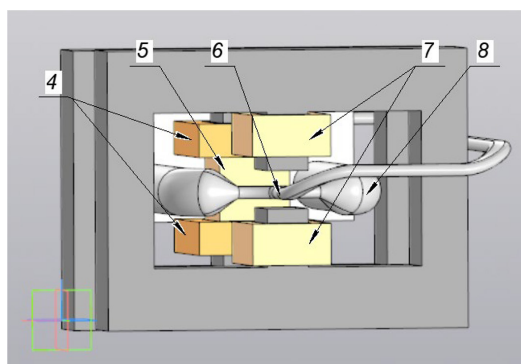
Конструкция электромагнитного насоса, вид спереди (футеровка скрыта), где: 4 – дополнительные катушки основного индуктора; 5 – основной индуктор; 6 – тройниковая рабочая зона; 7 – катушки электромагнита; 8 – жидкий металл
